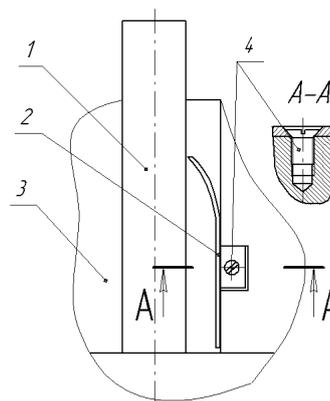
Конструкция приспособления с пластинчатыми пружинами
